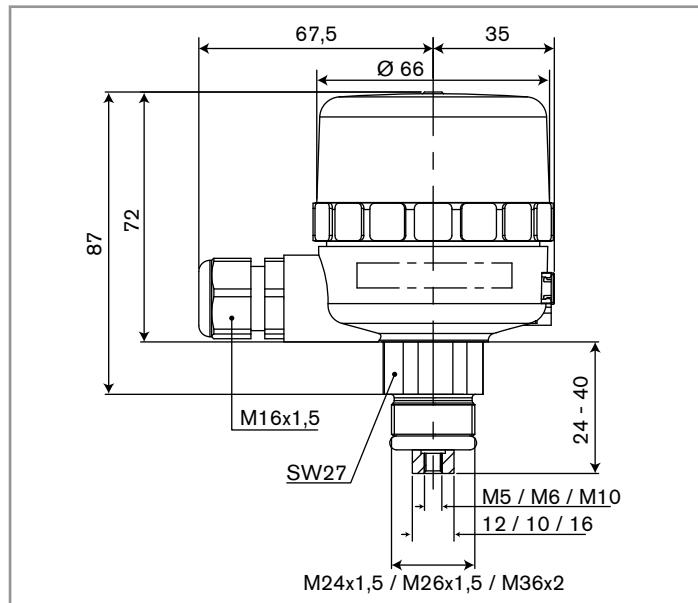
Dimensions de l'indicateur de position 1062 [mm]
